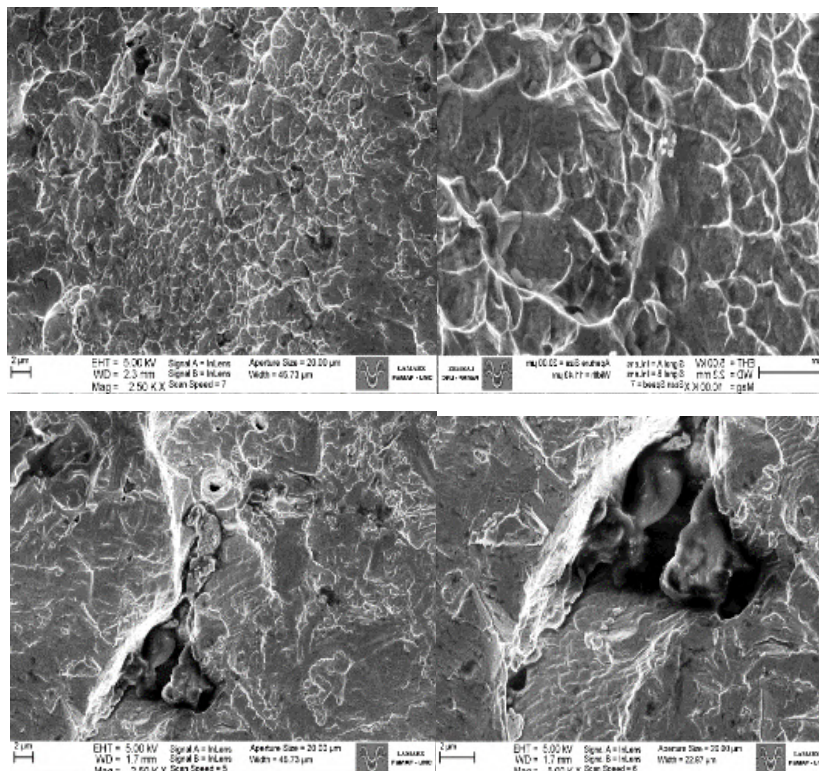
Detalles de la superficie de fractura de muestras del Grupo 2B.2 (limas TF flexionadas 60°). Dimples en la parte superior y facetas frágiles con estrías en la parte inferior.
